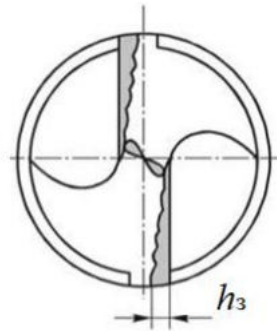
Знос свердла із швидкорізальної сталі при обробці ВЧКГ
